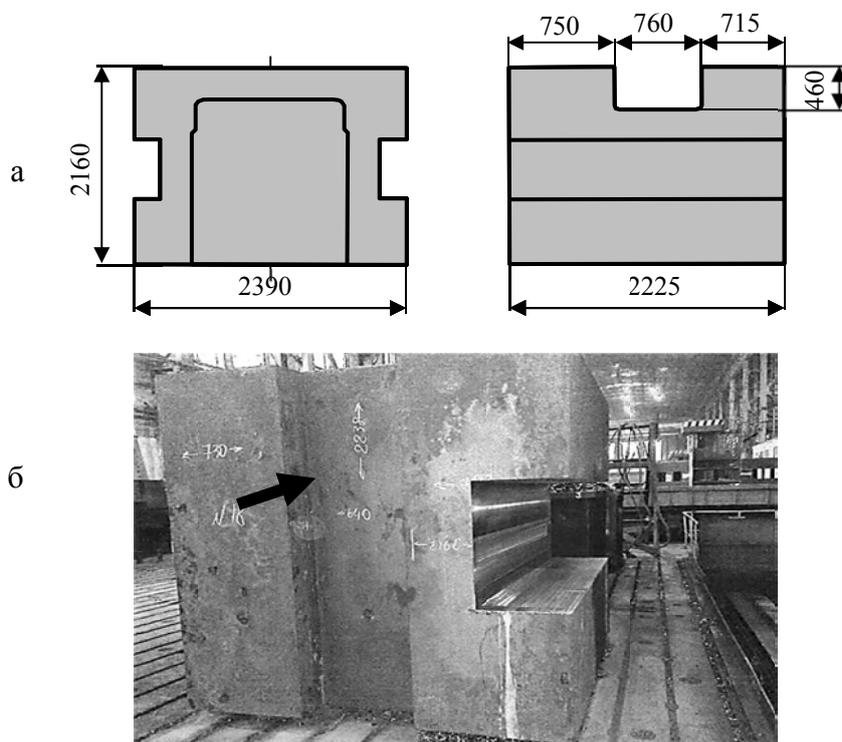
Выборка дефектного места в литой заготовке:
